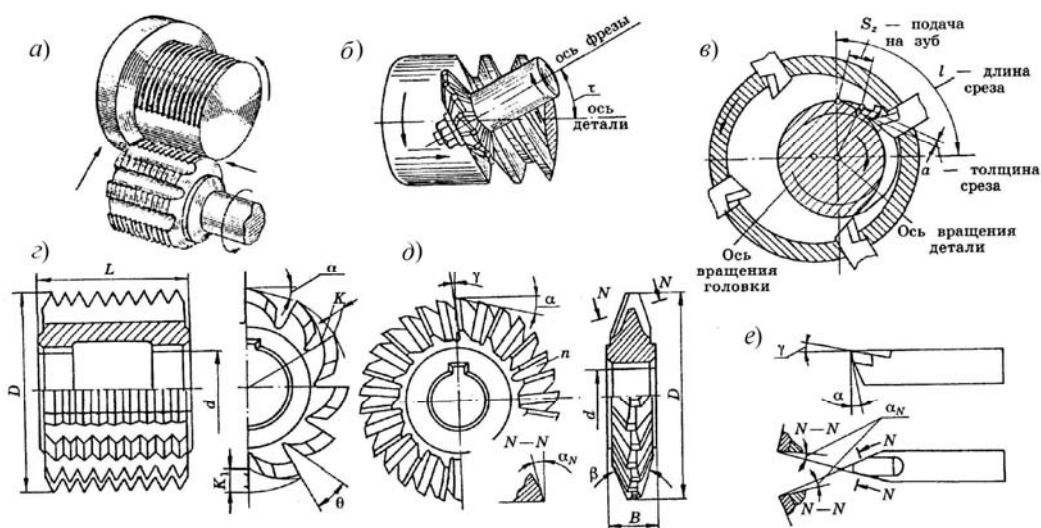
Схемы резьбофрезерования и соответствующие им инструменты
